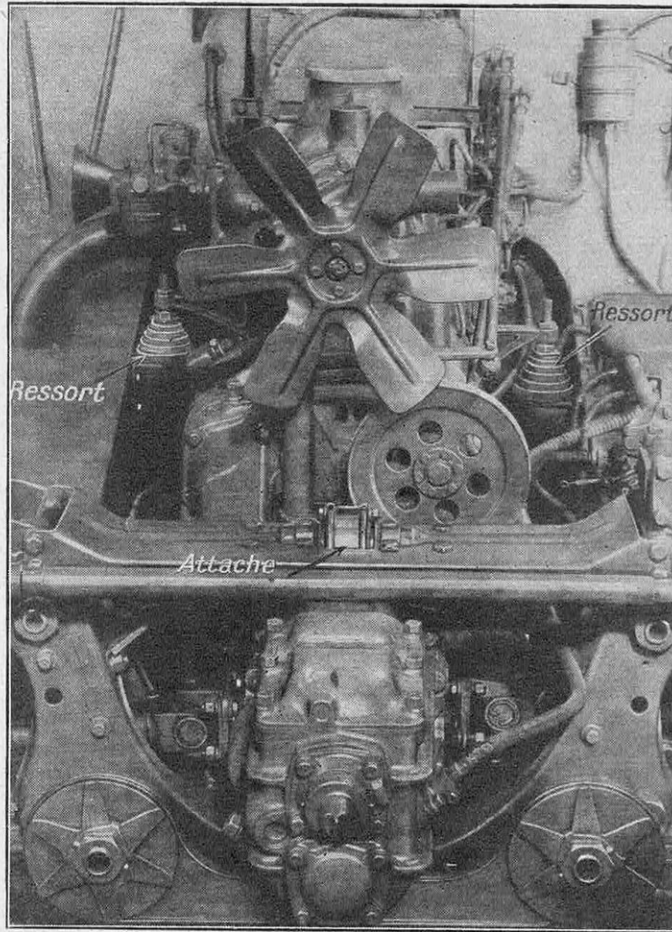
VUE AVANT D'UN MOTEUR MONTÉ SUR LE CHASSIS PAR LE DISPOSITIF « PAUSODYNE »
